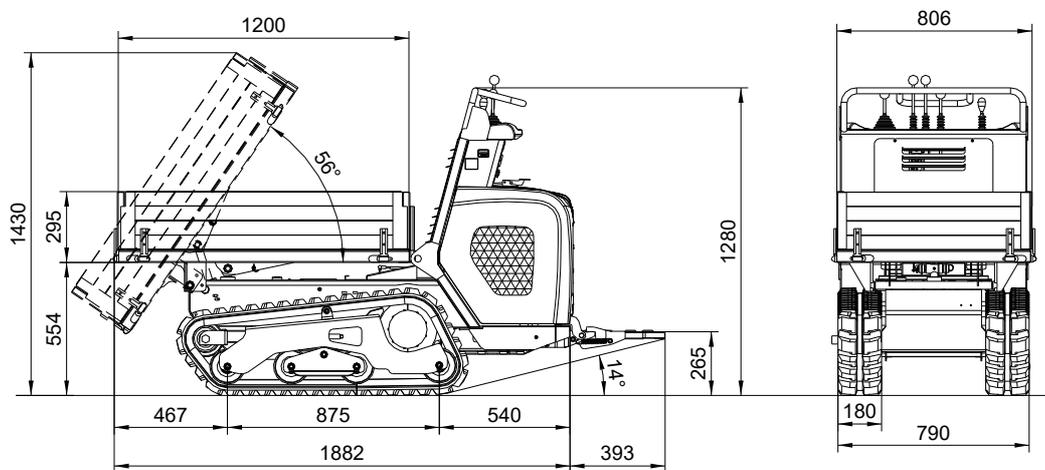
Fahrzeugabmessungen (Typ DT10 mit Frontkippmulde)
